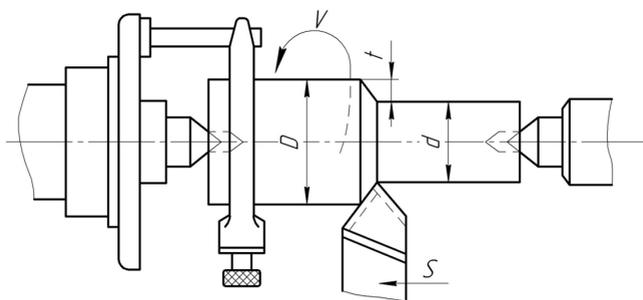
Схема токарной обработки цилиндрической поверхности:
